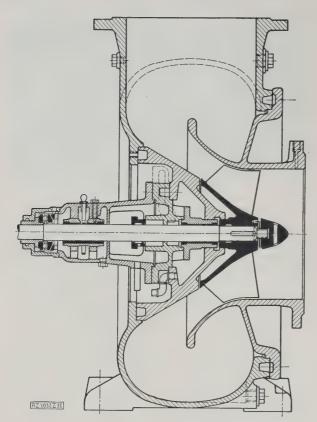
Schraubenpumpe von Klein, Schanzlin & Becker.
